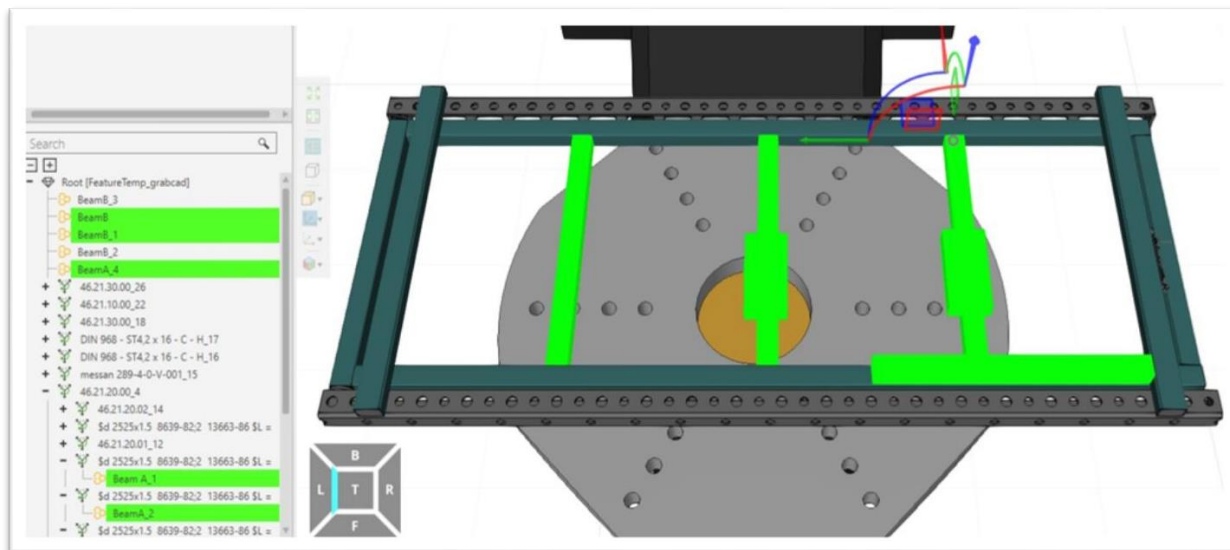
САD-модели заготовки со всеми подобными деталями в виде отдельной геометрии и названными аналогично
